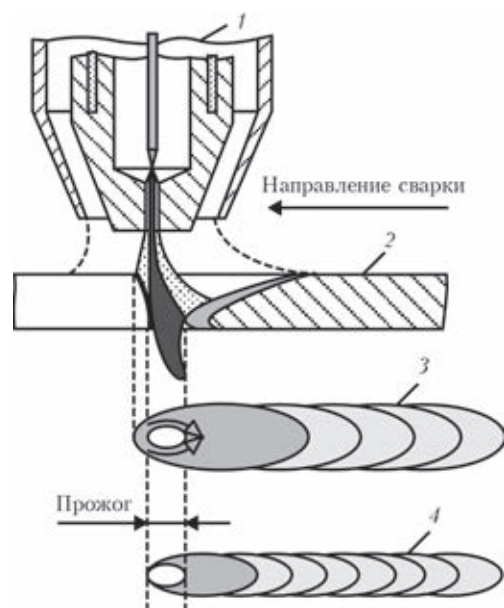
Принципиальная схема процесса плазменно-дуговой сварки в режиме «замочная скважина» (схема ISF Aachen) [22]: 1 — плазменная горелка; 2 — шов; 3 — поверхность шва; 4 — корень шва)
